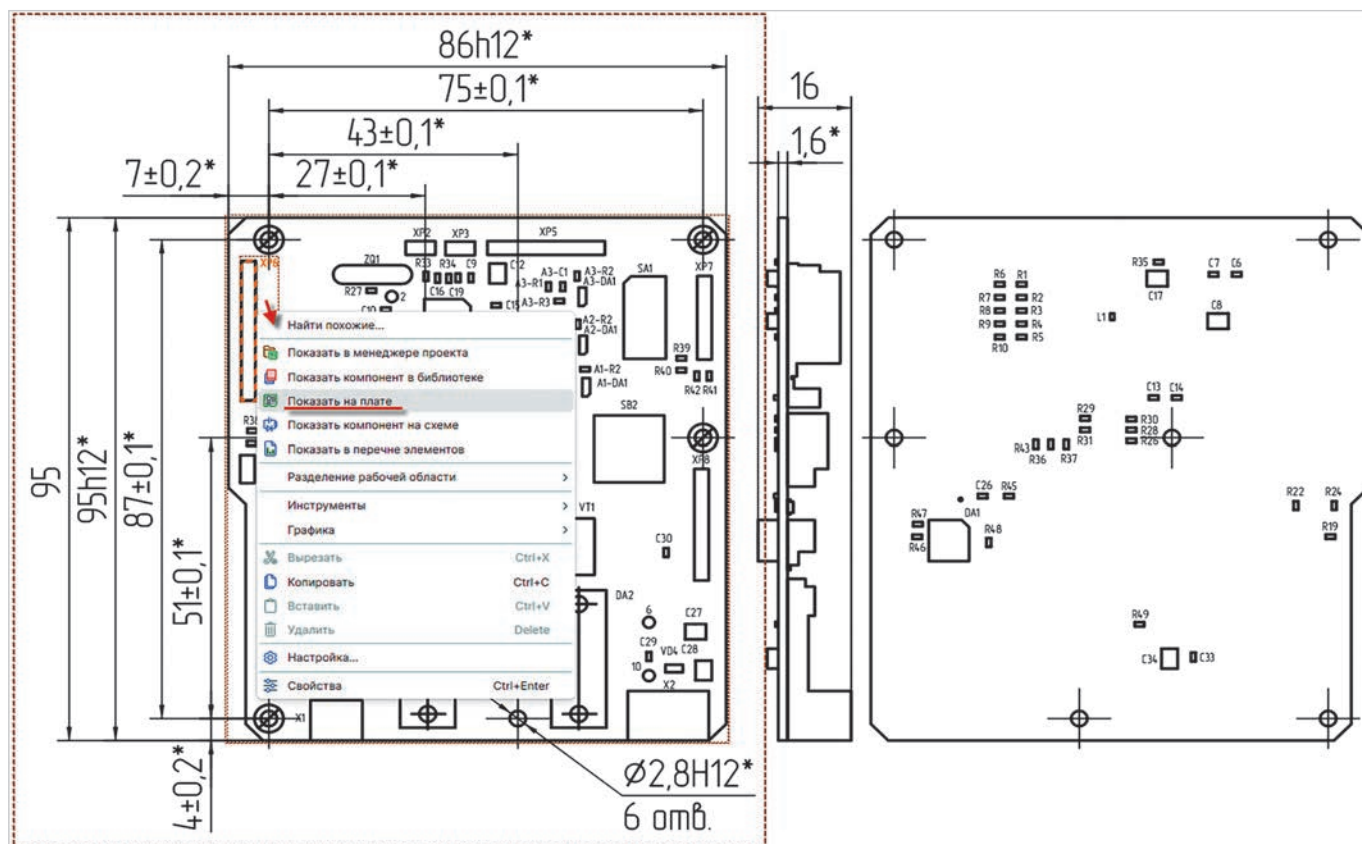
Сборочный чертёж ПУ. Виды печатной платы с компонентами
